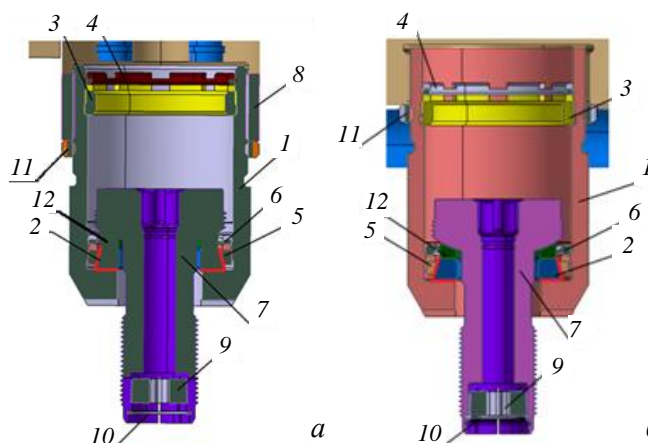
Система крепления ППС внешнего blankets (а), ППС blankets, расположенного на верхнем своде вакуумной камеры (б): 1 — стакан; 2 — шайба с ЭИП; 3 — транспортировочная шайба; 4 — стопорное резьбовое кольцо; 5 — фиксирующая гайка шайбы с ЭИП; 6 — стопорное резьбовое кольцо; 7 — болт; 8 — промежуточная обечайка; 9 — коническая резьбовая втулка; 10 — стопорное кольцо; 11 — гайка шлицевая; 12 — шайба сферическая
